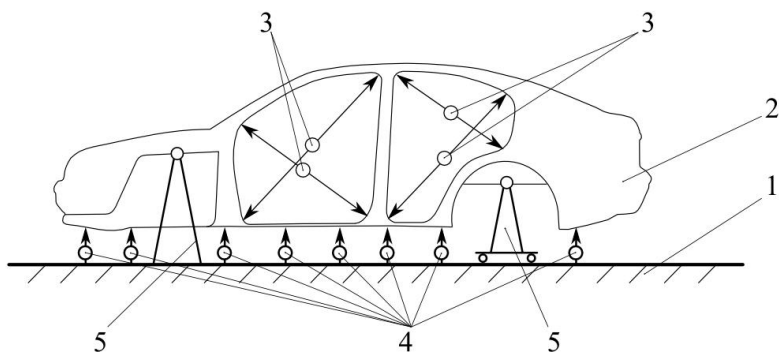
Схема стенда для испытания несущего кузова автомобиля на изгиб:
